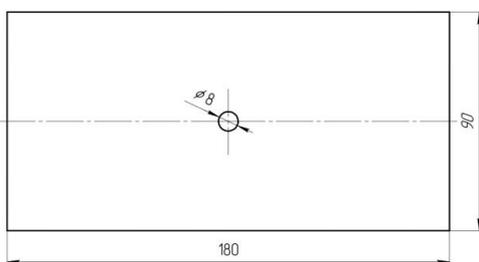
Фронтальное изображение корпуса приспособления для полировки
